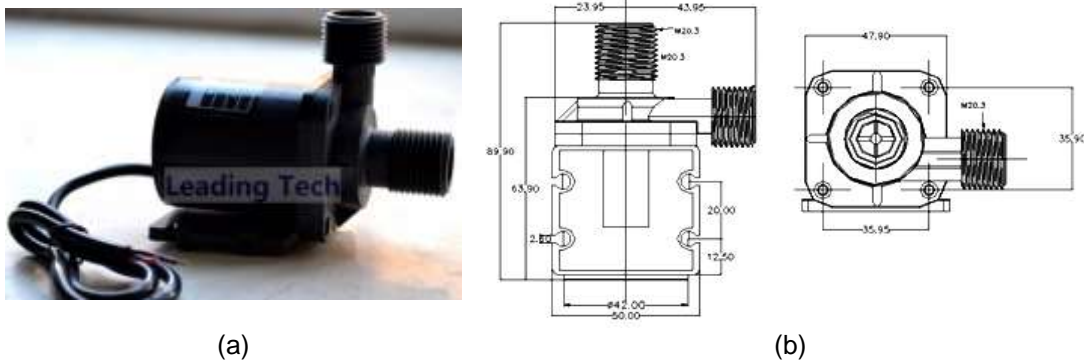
Bomba utilizada; a) foto do equipamento e b) dimensões da bomba
